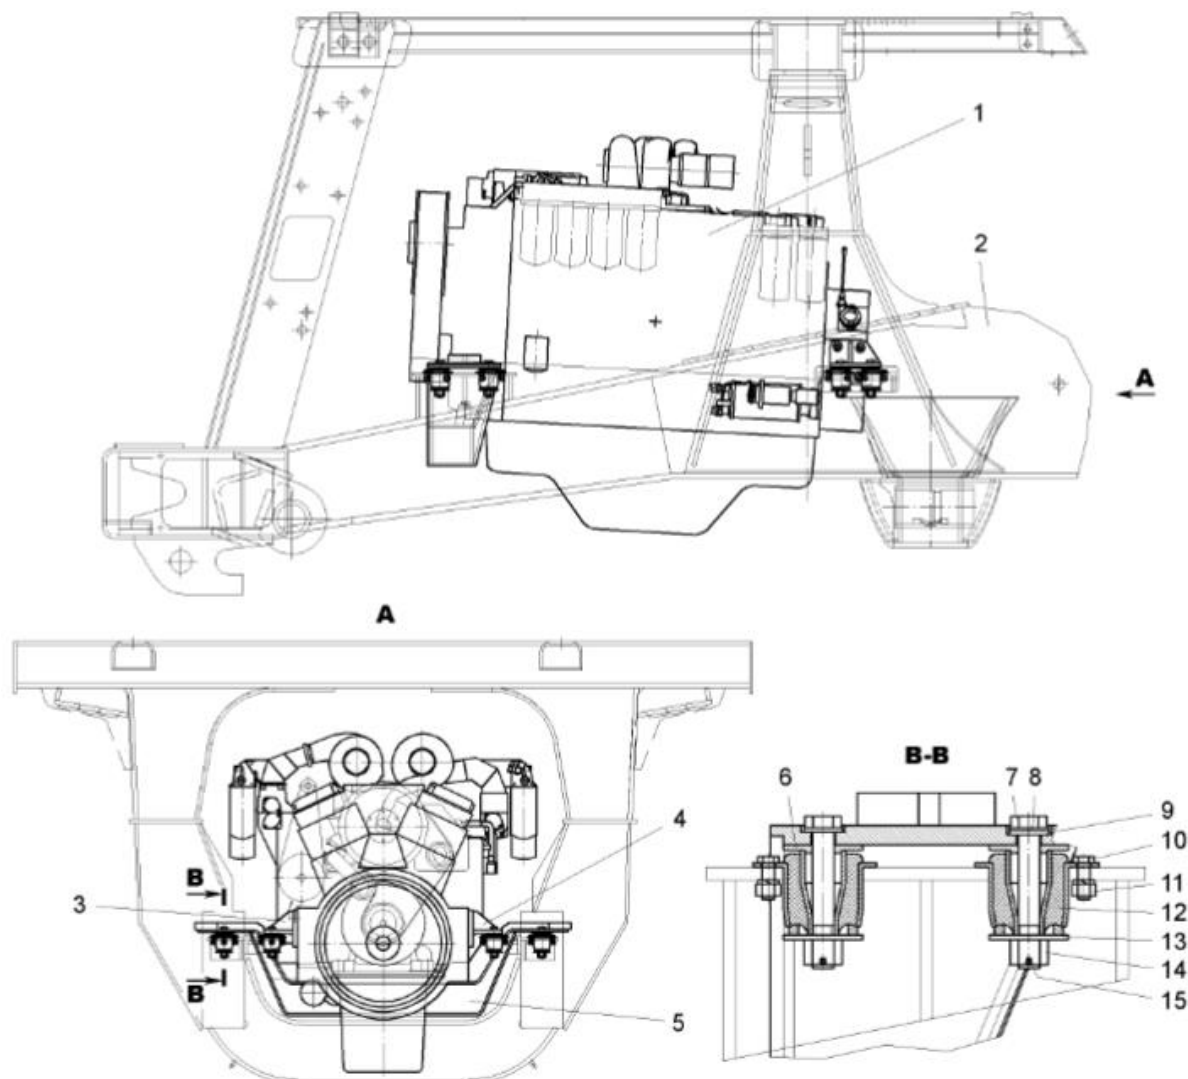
Установка ДВС на КС с гидромеханической трансмиссией: 1 – двигатель; 2 – рама самосвала; 3 – кронштейн задний левый; 4 – кронштейн задний правый; 5 – балка передней опоры двигателя; 6 – шайба центрирующая; 7, 10 – болты; 8, 9 – шайбы регулировочные; 11, 14 – гайки; 12 – опора коническая; 13 – шайба; 15 – шплинт.
